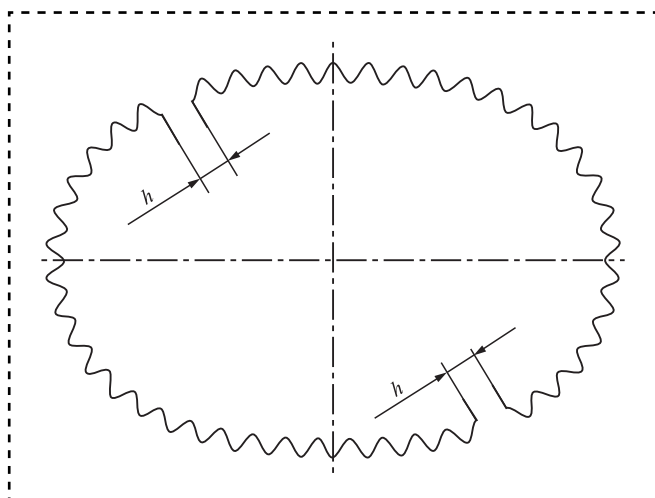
Солнечная шестерня ПРМ схемы 3-2 с каналами в цилиндрической зубчатой поверхности
